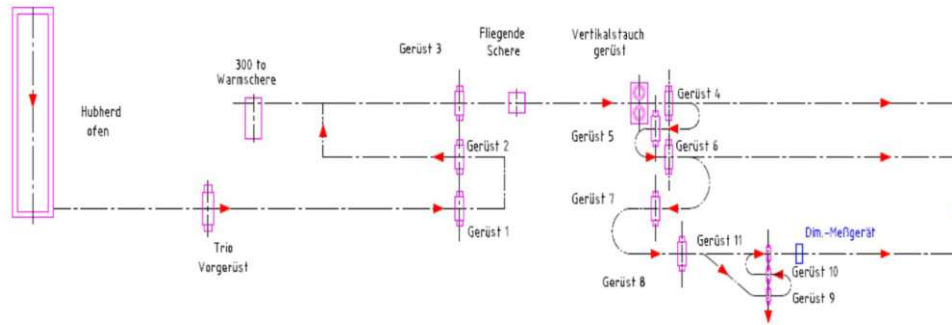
Schematische Darstellung eines Teils der Walzstraße: Hubherdofen, Walzgerüste.
